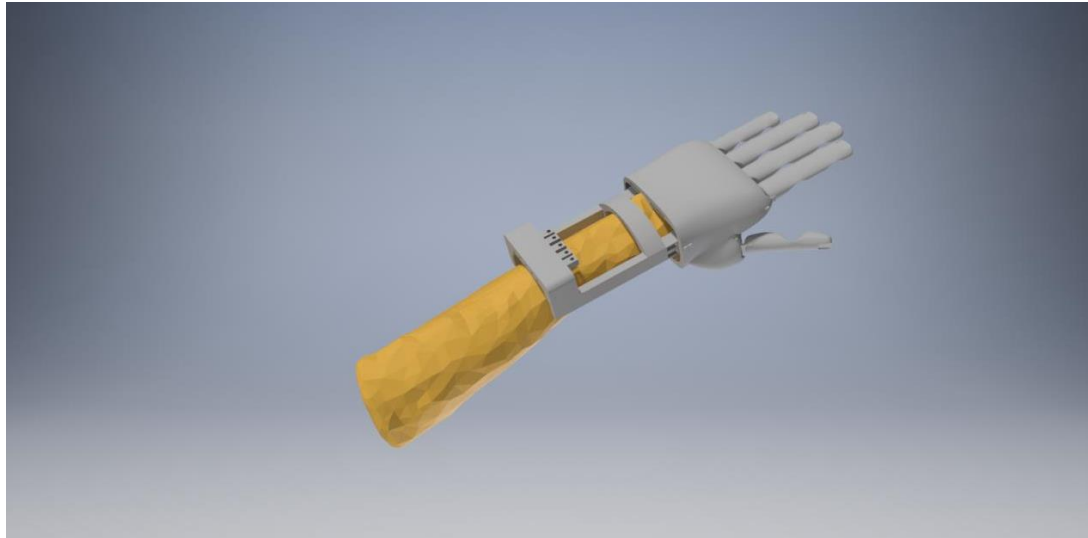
Ensamblaje de la prótesis junto el brazo escaneado
